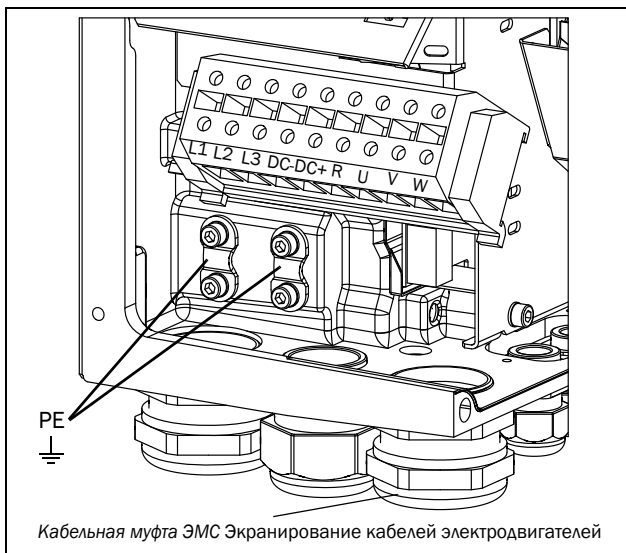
Подключение сетевого питания и двигателя модели 026-046, типоразмер корпуса С
